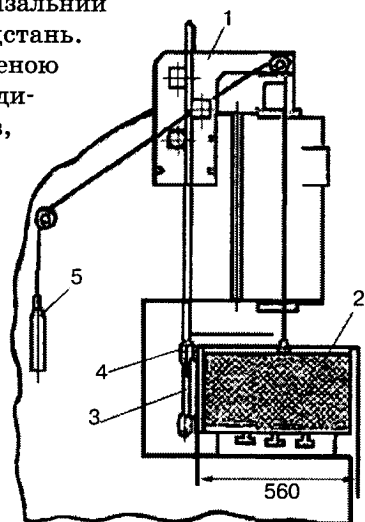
Захисний пристрій підйомного типу до вертикально-фрезерного верстата:
